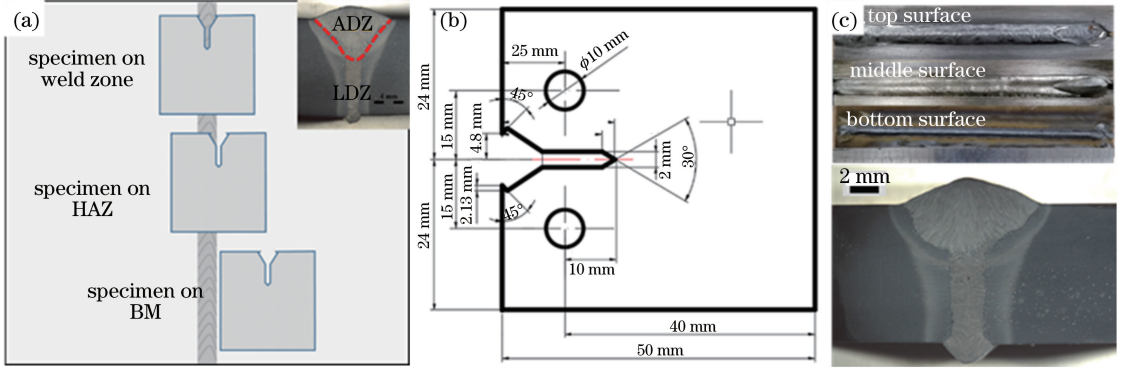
CT 试样。(a)取样位置;(b)试样尺寸;(c)焊缝形貌
